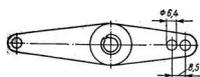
Схема расположения отверстий в двуплечем рычаге тормозной педали
